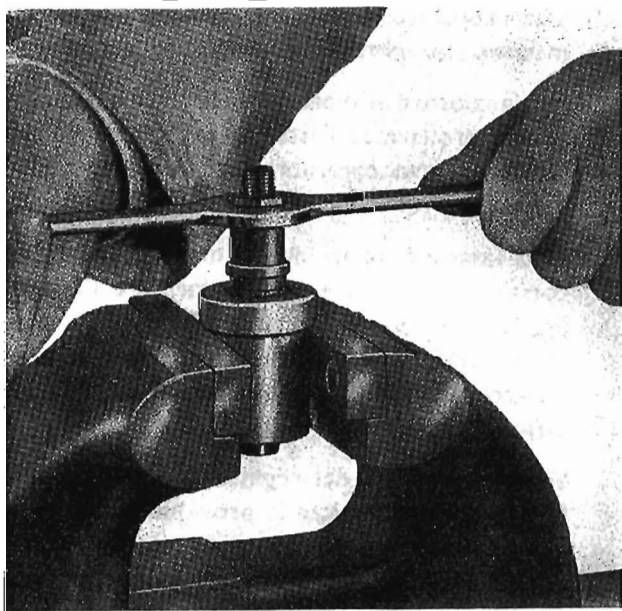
Smontaggio e rimontaggio dell'iniettore nel supporto A 323023.
